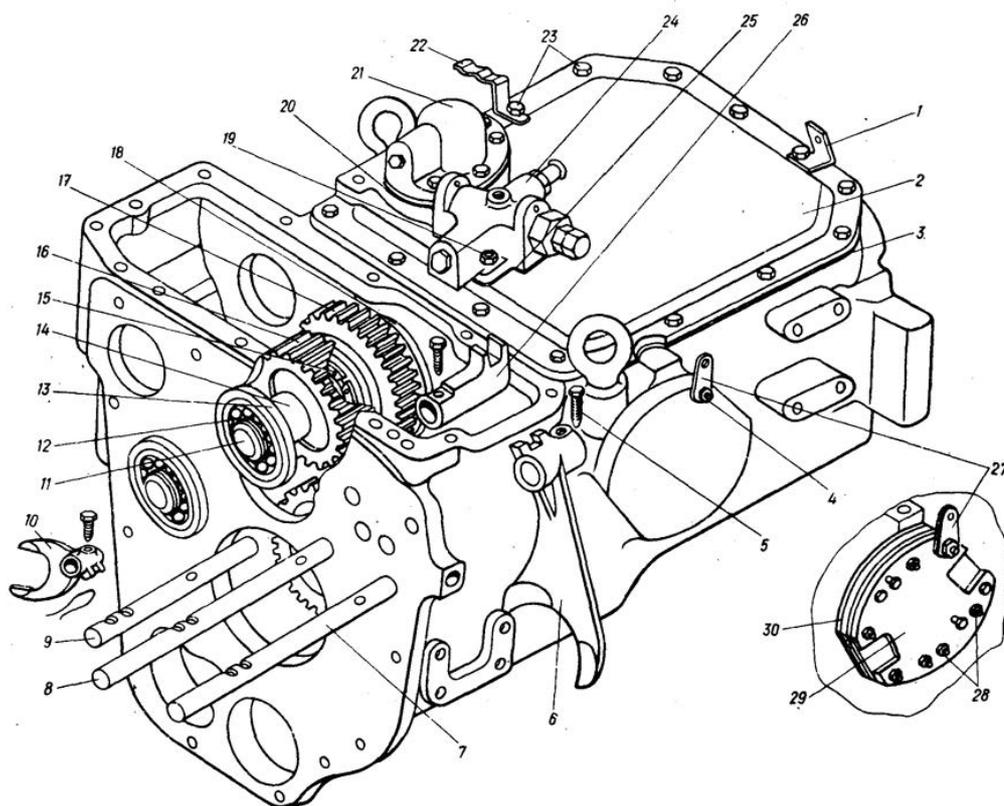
Установка крышки, распределителя, зубчатых колес заднего хода:
